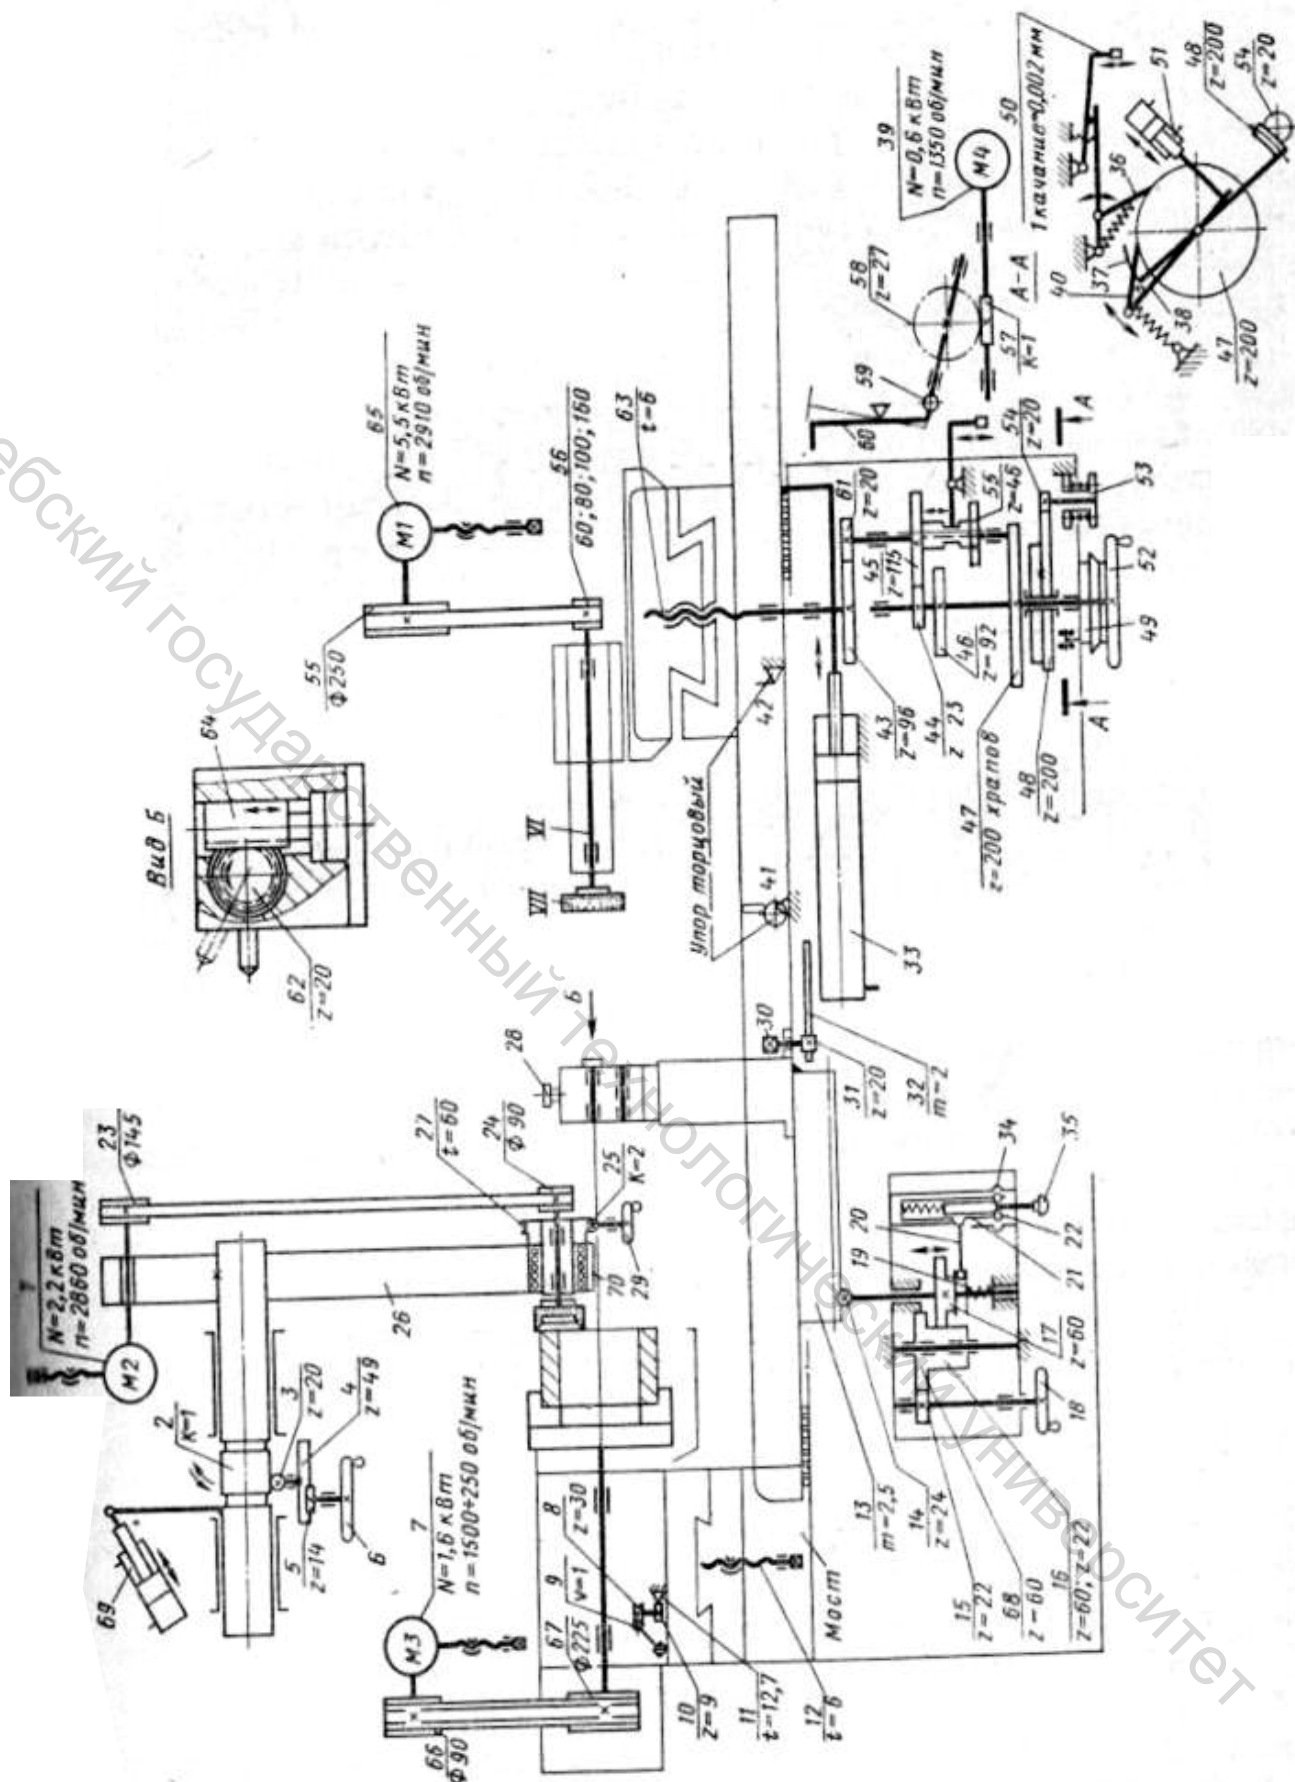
Кинематическая схема универсального внутришлифовального станка мод. 3К228В
